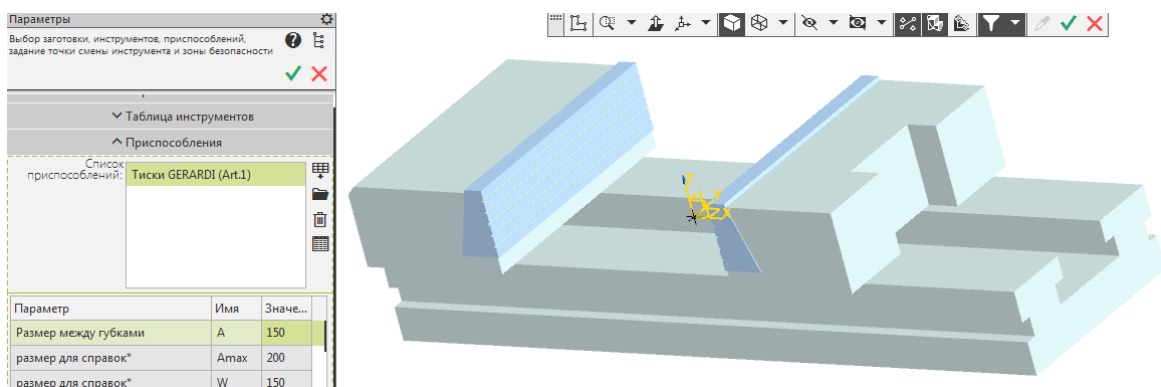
Вибір пристосування для закріплення заготовки
